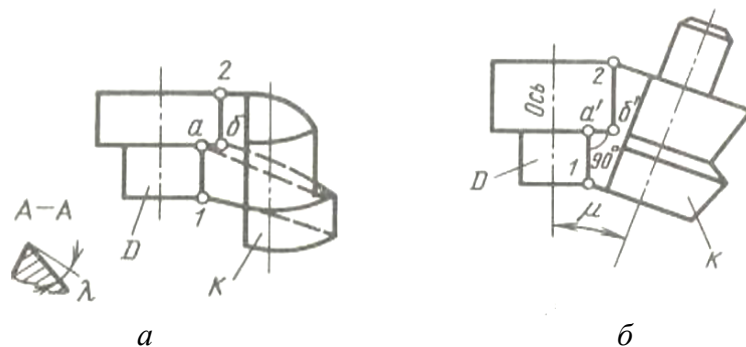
Фасонні різці з похилим установленням і гвинтовою задньою поверхнею
